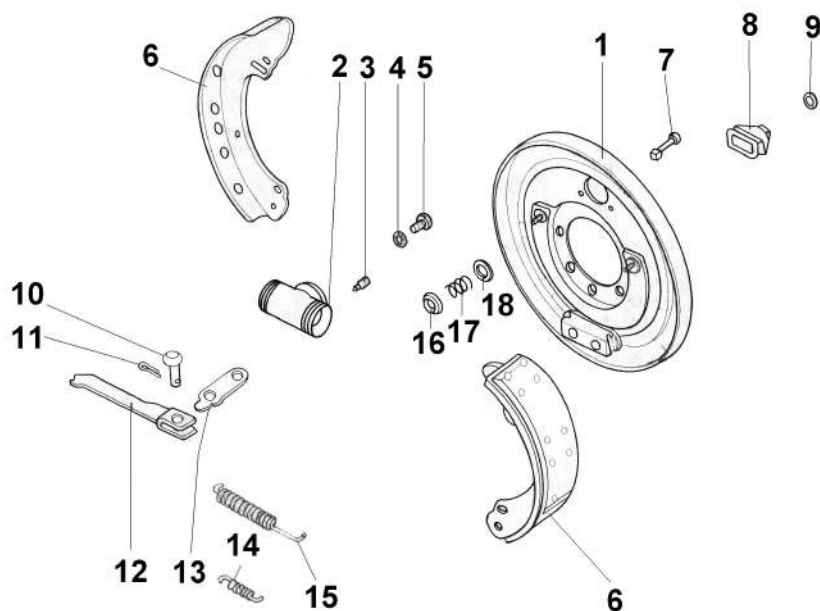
Устройство заднего тормоза: 1- тормозной щит; 2- рабочий цилиндр; 3- штуцер прокачки; 4- шайба; 5- болт крепления цилиндра; 6- тормозные колодки; 7- опорная стойка; 8- резиновый чехол; 9- кольцо; 10- палец; 11- шплинт; 12- приводная штанга; 13- приводной рычаг; 14 и 15- стяжные пружины; 16- стакан; 17- пружина; 18- тарелка пружины
